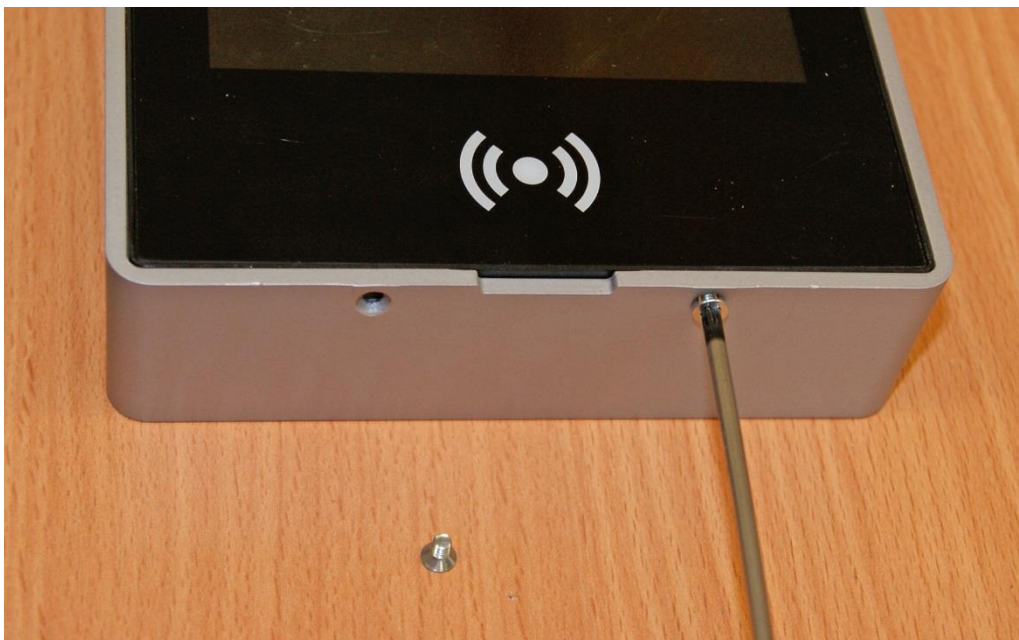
Entfernen der Schraube unten im Einbaurahmen
